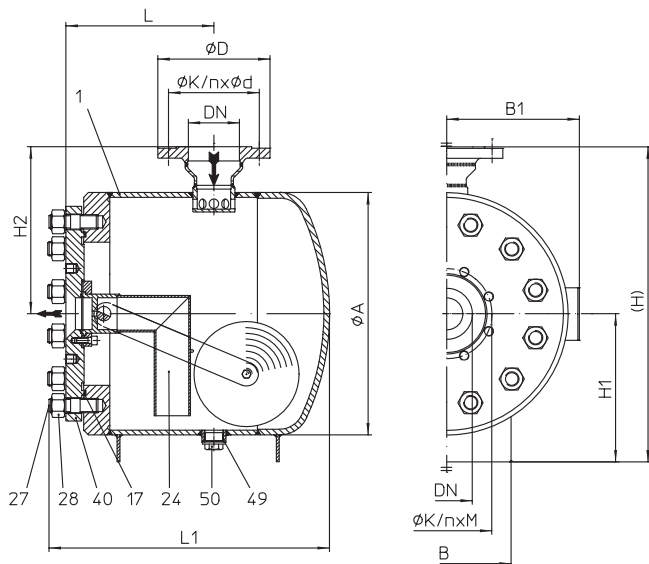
1 Konstrukcja kątowa z kolierzami -
